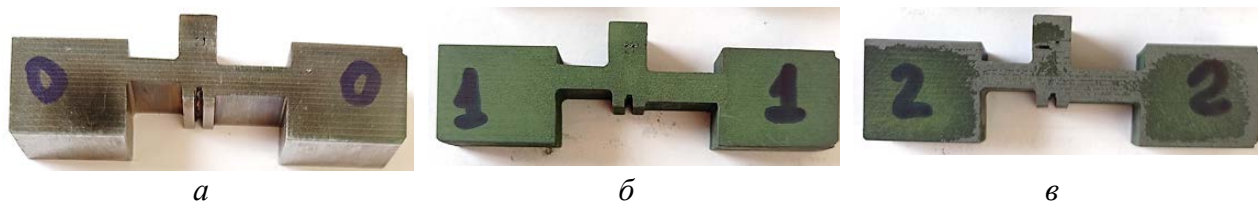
Общий вид сварных образцов сплава ВЖ172-ИШ
